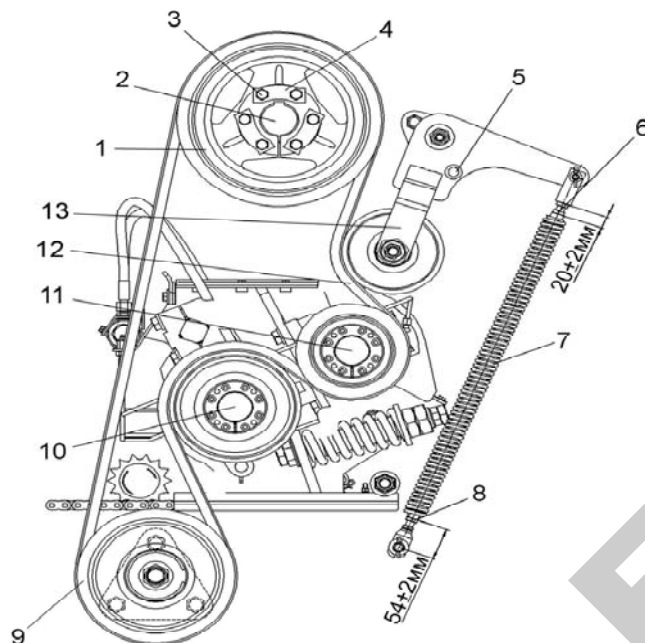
Регулировка привода доизмельчающего устройства:
